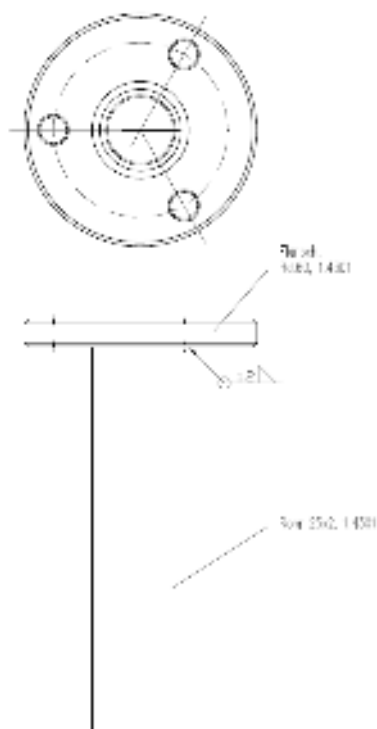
Tauchhülse mit Einschraubgewinde für SS27 und MS27
